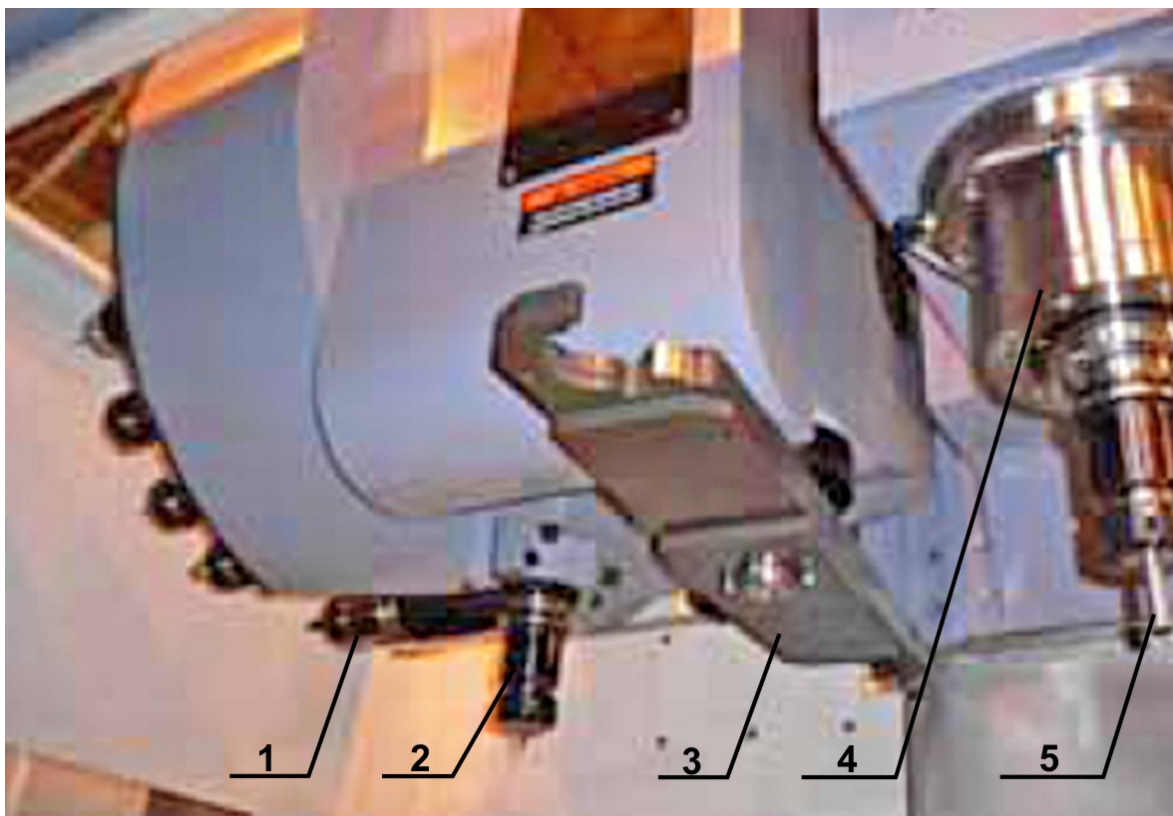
Инструментальный магазин типа «*ПУКА*» (вид со стороны манипулятора):
